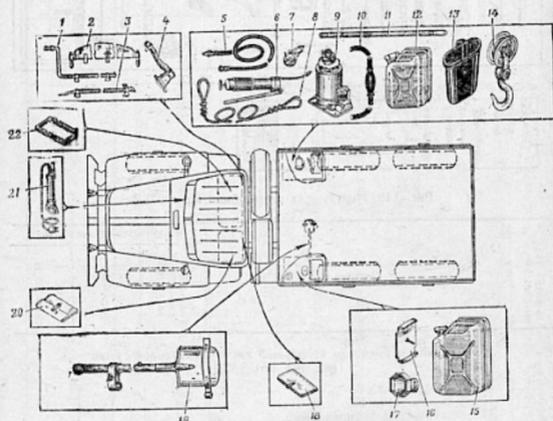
Раскладка инструмента и принадлежностей автомобиля Урал-375Д
